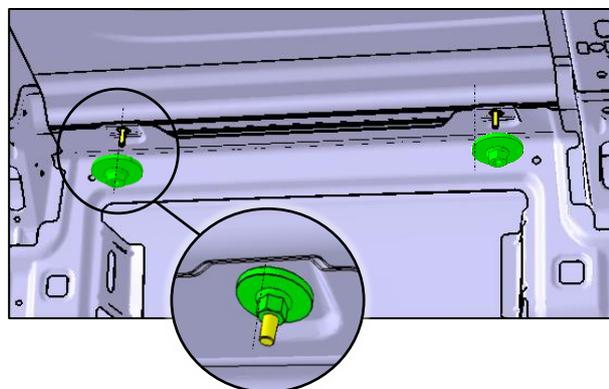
vista dall'interno dei punti di collegamento a vite zona tetto
